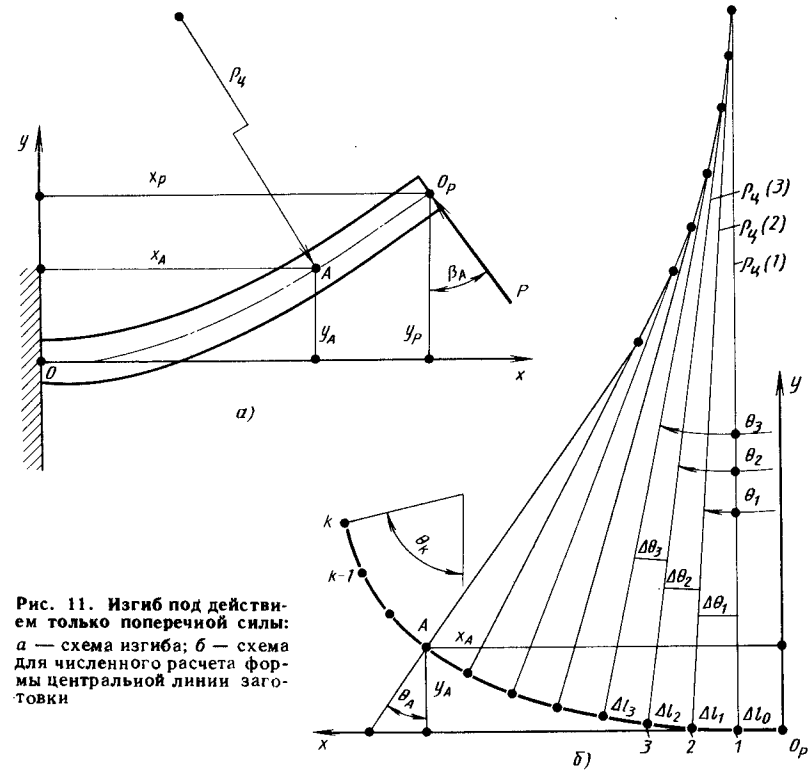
Изгиб под действием только поперечной силы: а — схема изгиба; б — схема для численного расчета формы центральной линии заготовки
